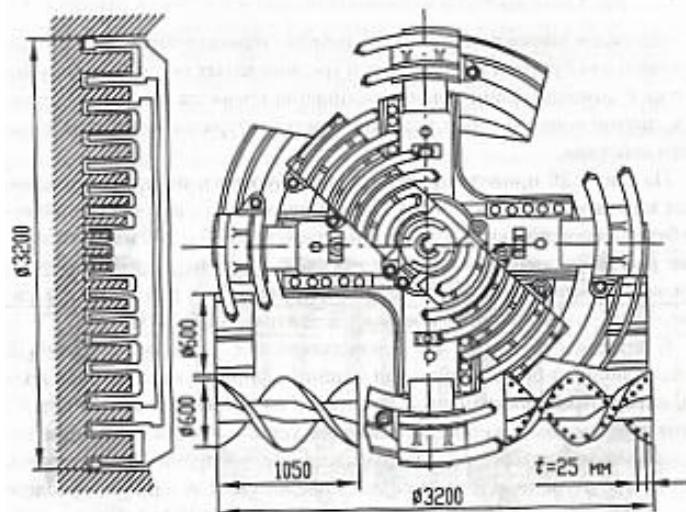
Исполнительный орган проходческого комбайна ПК8 режуще-скальвающего типа
